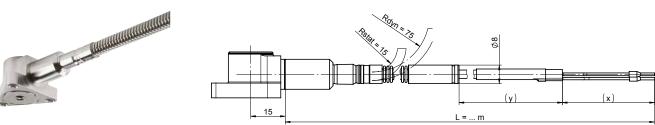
8205BxxEDJxx: hermetisch dichter Wellschlauch
